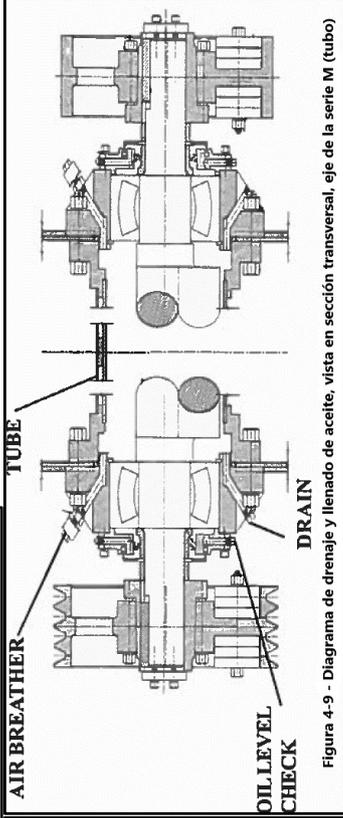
Diagrama de drenaje y llenado de aceite, vista en sección transversal, eje de la serie M (tubo)
